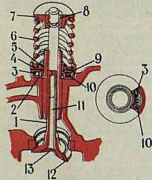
Механизм вращения выпускного клапана двигателя ЗИЛ-130: 1 — клапан; 2 — неподвижный корпус; 3 — шарик; 4 — упорная шайба; 5 — замочное кольцо; 6 — пружина; 7 — тарелка; 8 — сухари; 9 — дисковая пружина; 10 — возвратная пружина; 11 — натриевое наполнение; 12 — жаропрочная наплавка; 13 — заглушка.
